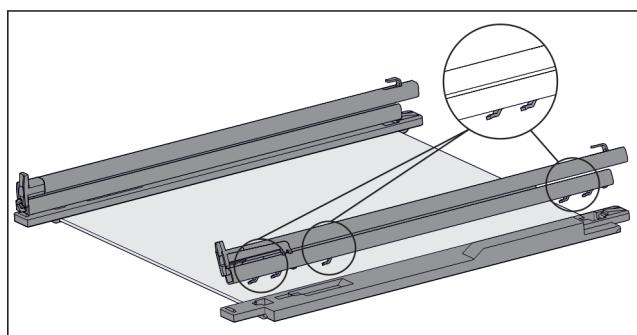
Скляна пластина з рейками та деталями для підтримки
